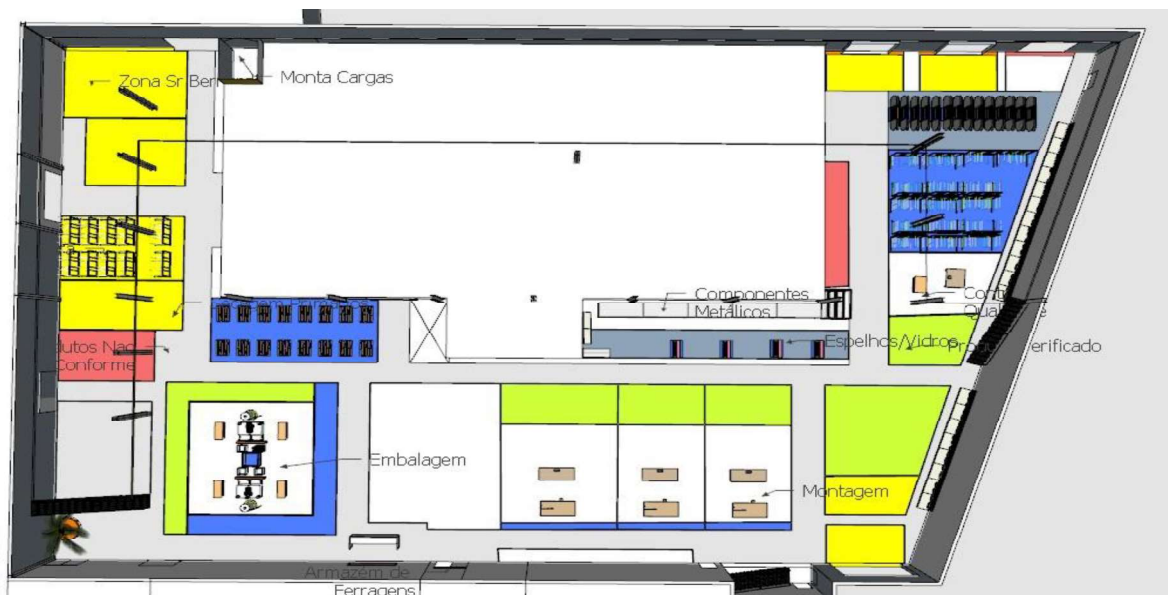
Layout do setor de Embalagem - Vista de Cima
